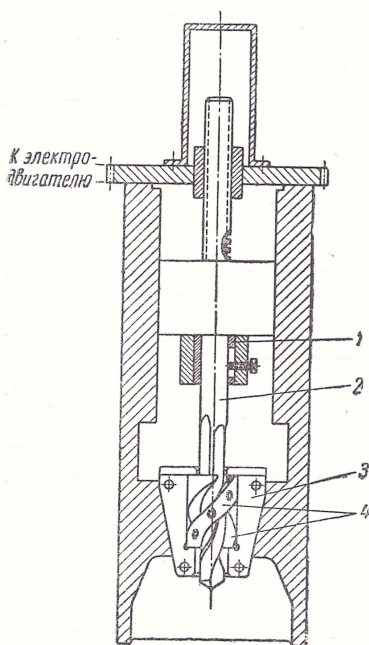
Схема завивки заготовок сверл на винтовом прессе при помощи матрицы
